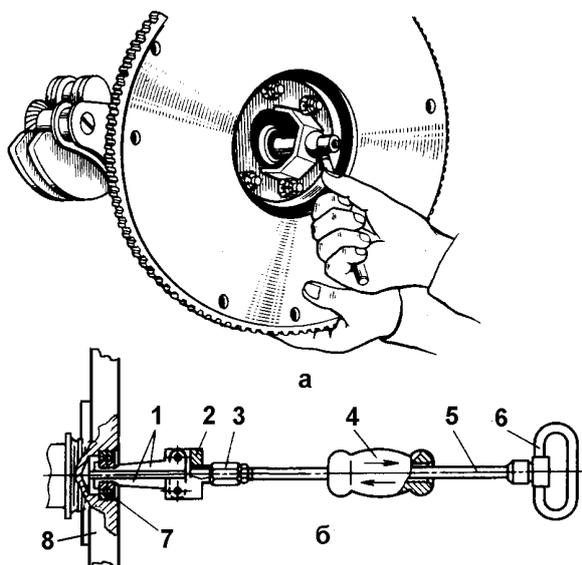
Выпрессовка переднего подшипника первичного вала коробки передач при помощи съемника:
